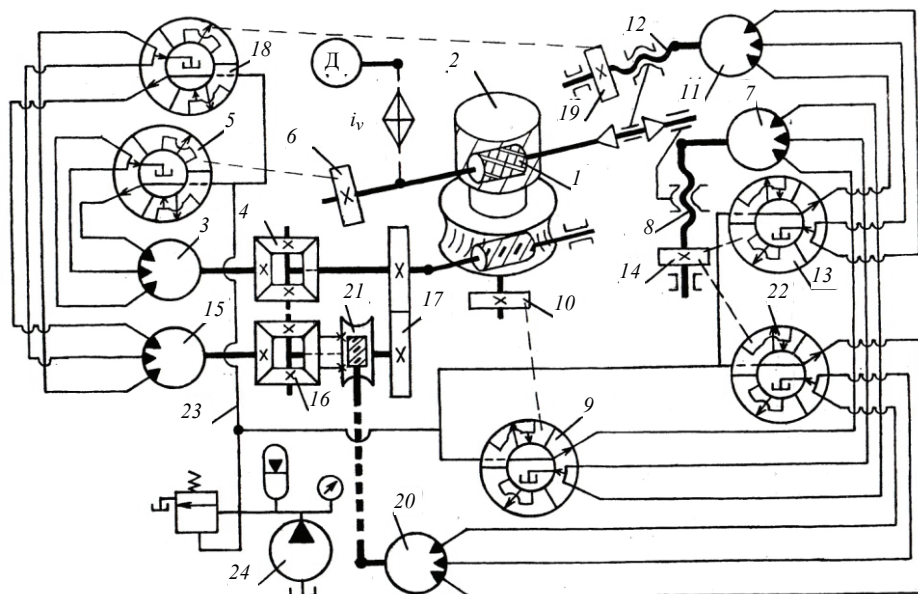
Структурная схема зубофрезерного станка с гидравлическими внутренними связями для нарезания зубьев цилиндрических зубчатых колес методом диагональной подачи
